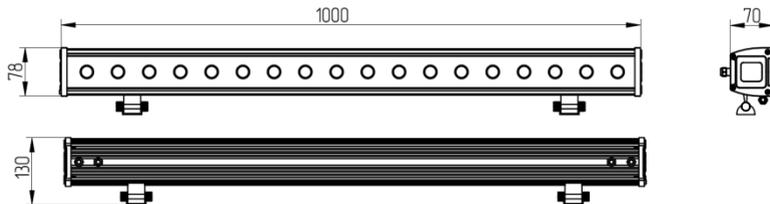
Габаритные размеры линейного прожектора RGBW 72W.
